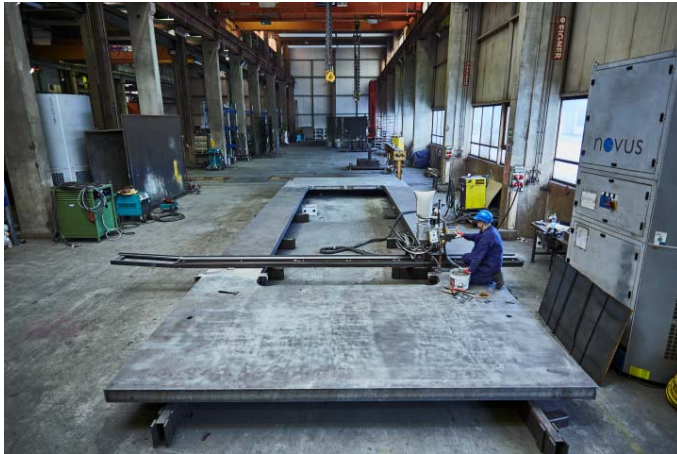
Schuler beauftragte Jebens als führenden Spezialisten für große schwere Brennzuschnitte und montagefertige Schweißbaugruppen mit der Fertigung der Pressenplatten.
